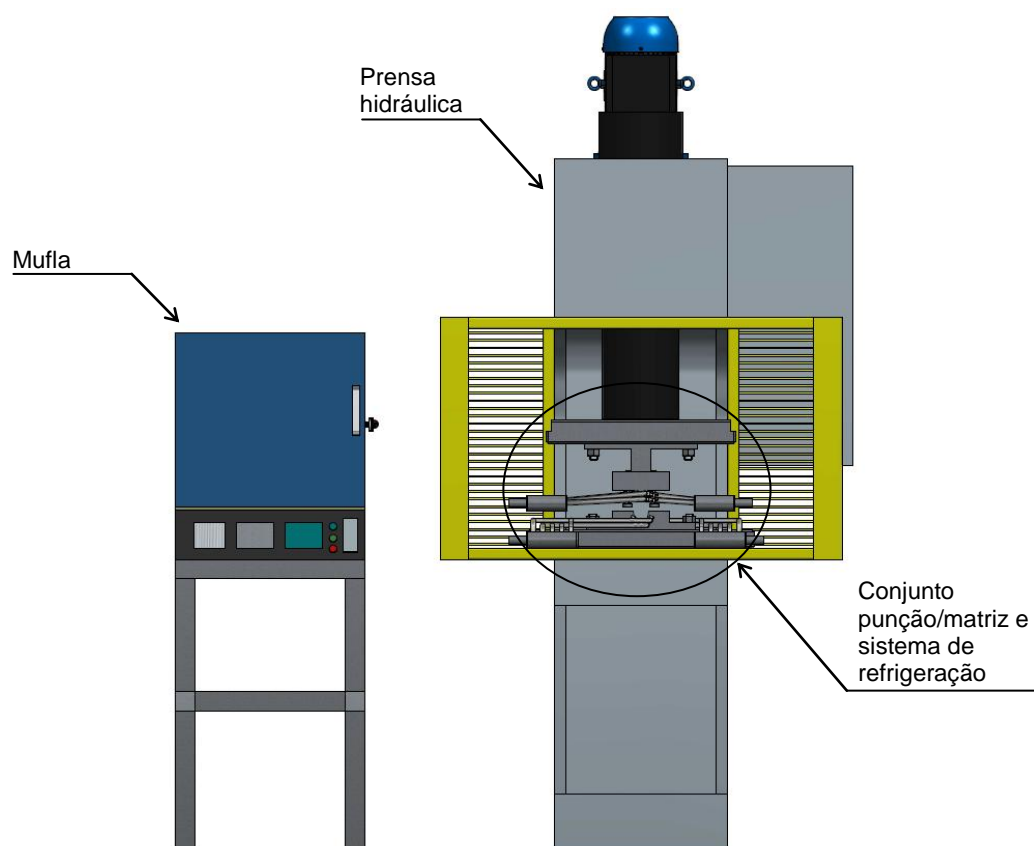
Desenho esquemático do equipamento piloto para estampagem a quente.
